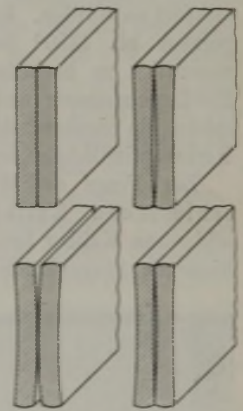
Wirkung des Verziehens bei Blättern mit genau rechteckigem (links) und hohl-gewalzt rechteckigem Querschnitt (rechts).
